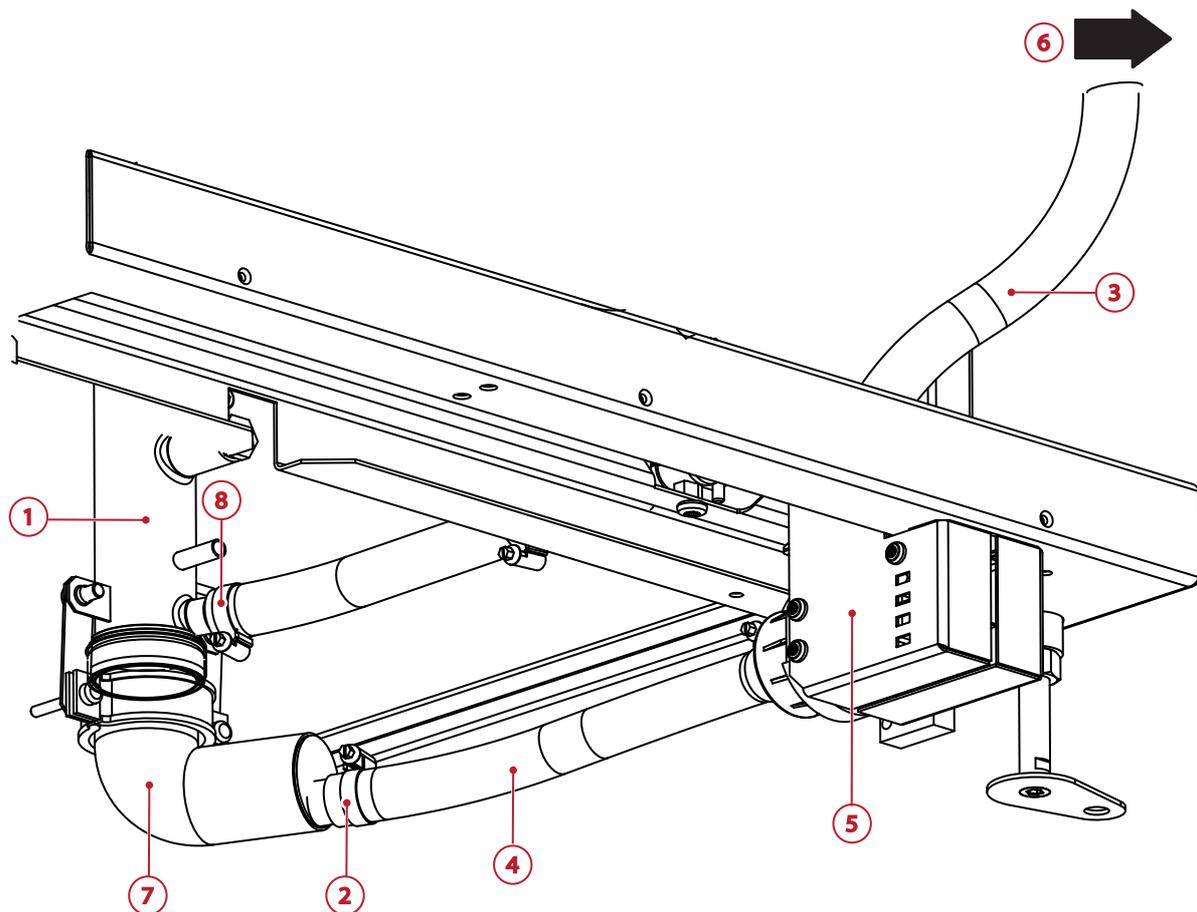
Maschinenablauf mit Ablaufpumpe
